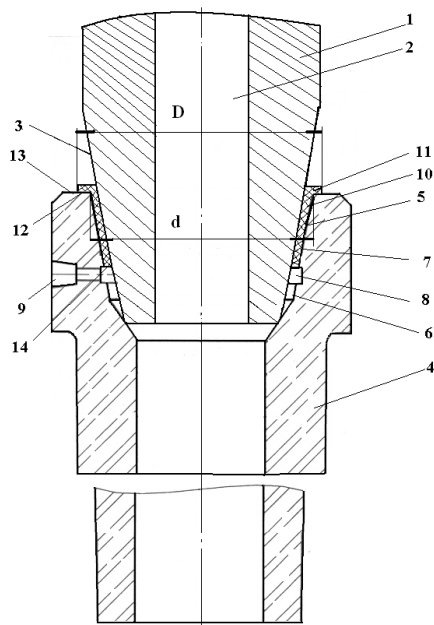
Устройства для защиты струи металла при разливке на МНЛЗ
